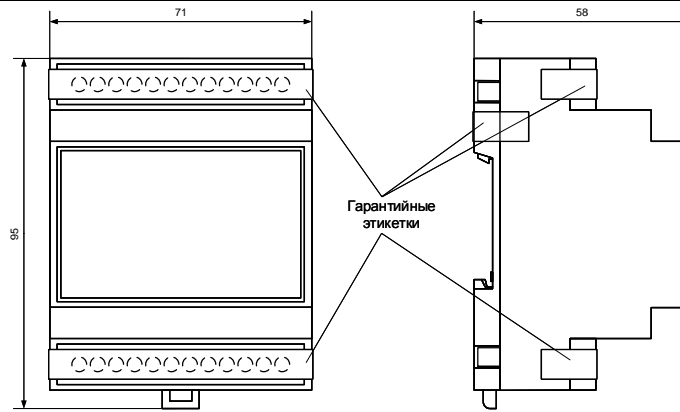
Внешний вид, габаритные и установочные размеры счетчика СИПУ xxx.10x.D
